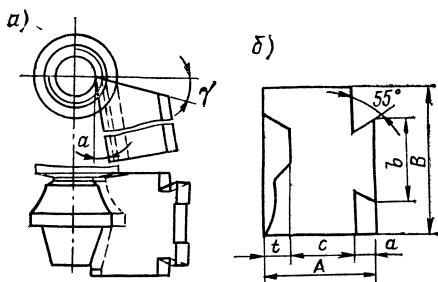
Призматический резец (с тангенциальным направлением подачи): a — установка относительно изделия; b — основные размеры резца; (A и B — толщина и ширина резца; a и b — высота и ширина ласточкина хвоста; c — толщина тела резца)
